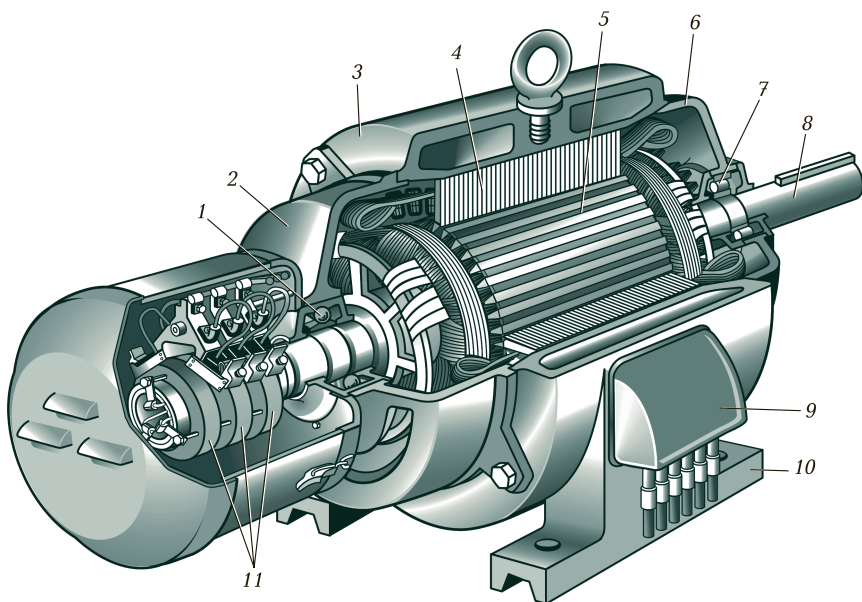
Устройство трехфазного асинхронного двигателя с фазным ротором:
